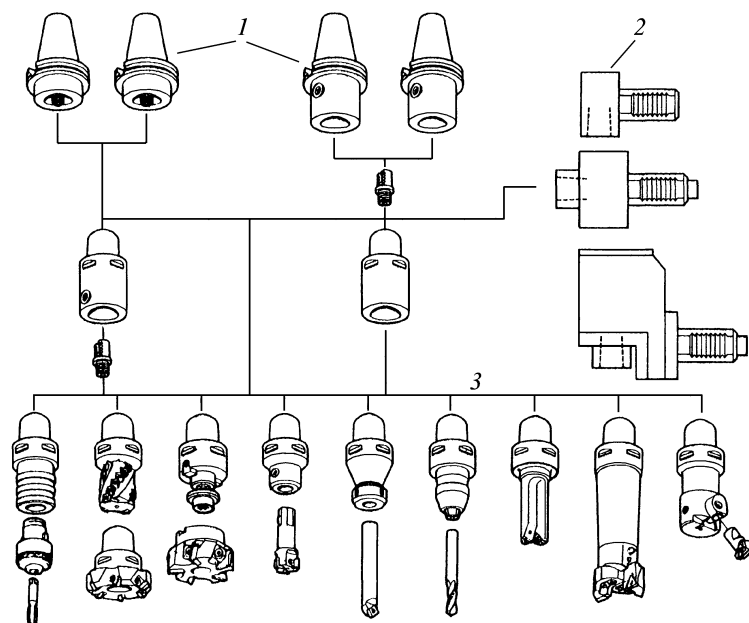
Патроны 1 и резцедержатели 2 для вращающегося инструмента 3
